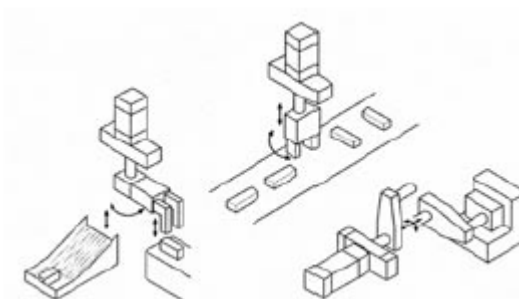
Kyvný motor s ozubeným hřebenem a pastorkem[1]
